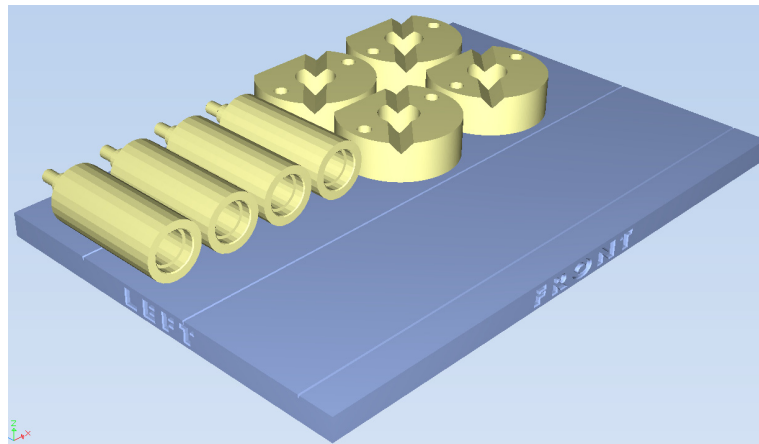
Disposition du plateau après l'application du plan de coupe
